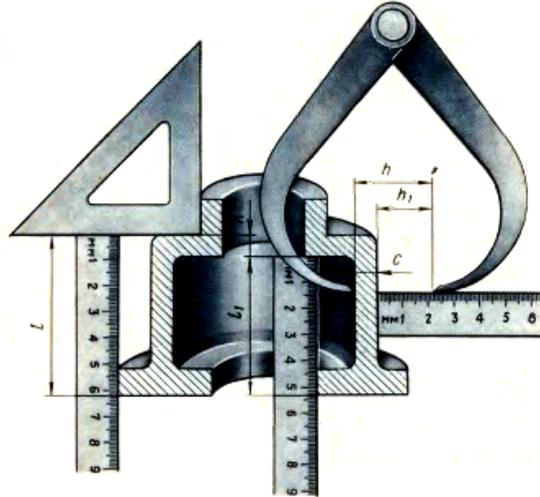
Вимірювання товщини дна й товщини стінки деталі
